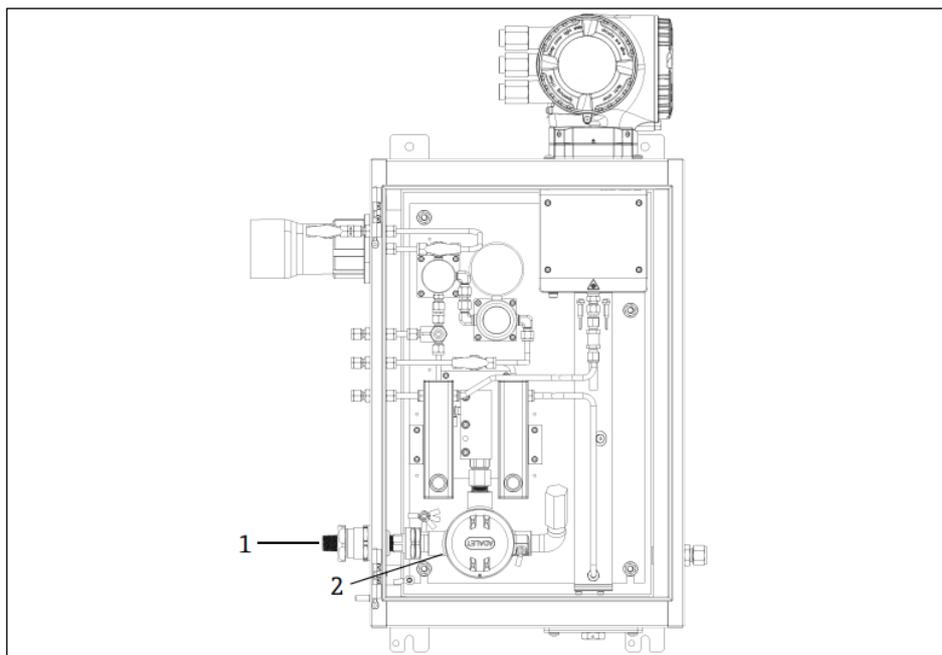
Силовой ввод обогревателя и соединительная коробка
